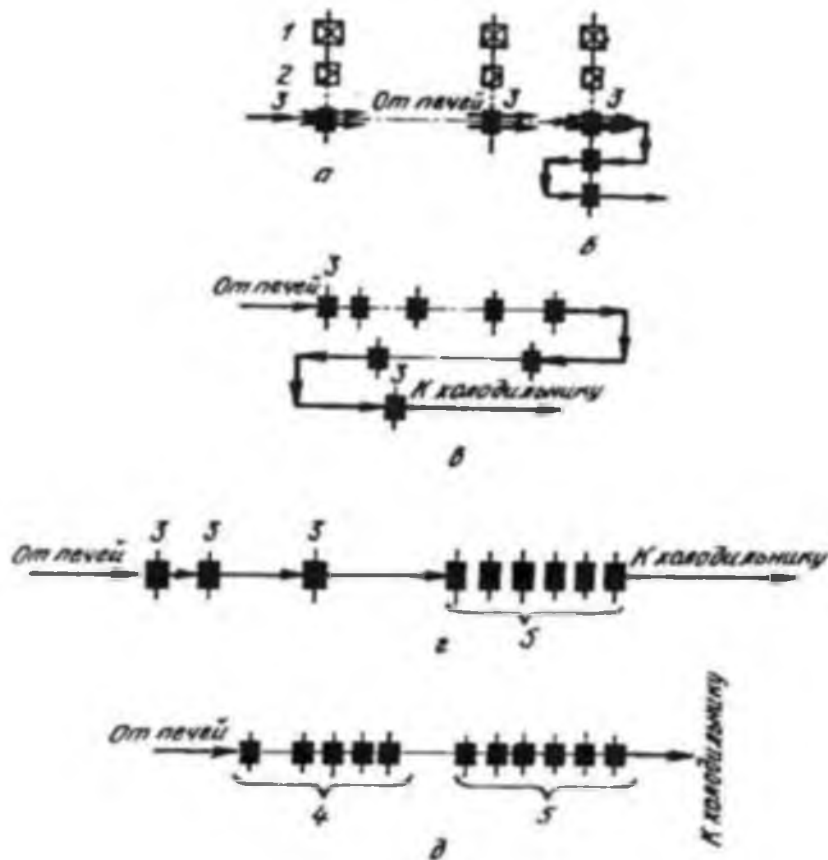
Схема расположения рабочих клеток прокатных станов:
